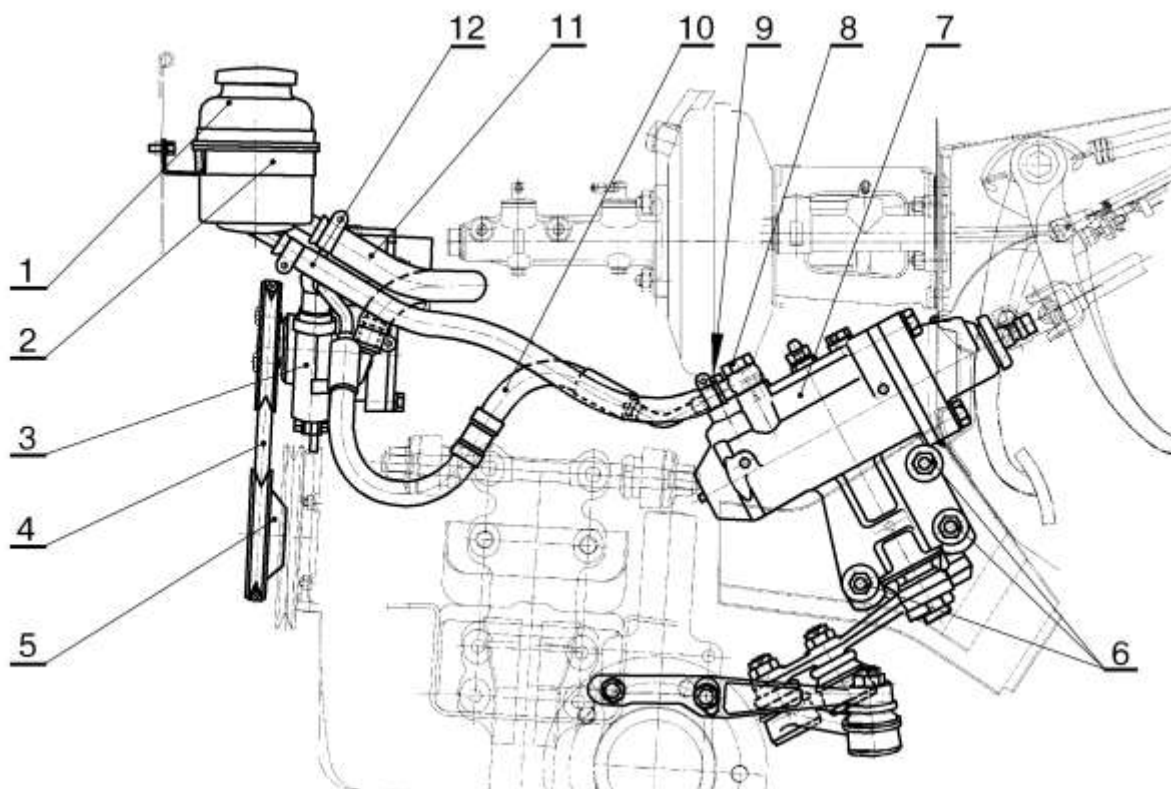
Схема расположения рулевого механизма с гидроусилителем на автомобиле ВАЗ–21213: 1 - бак масляный; 2 - кронштейн масляного бака; 3 - насос гидроусилителя; 4 - ремень привода насоса; 5 - шкив привода насоса; 6 - гайки крепления картера рулевого механизма; 7 - рулевой механизм; 8 - болт крепления шланга низкого давления; 9 - болт крепления шланга высокого давления; 10 - шланг высокого давления; 11 - шланг подводящий; 12 - шланг сливной
